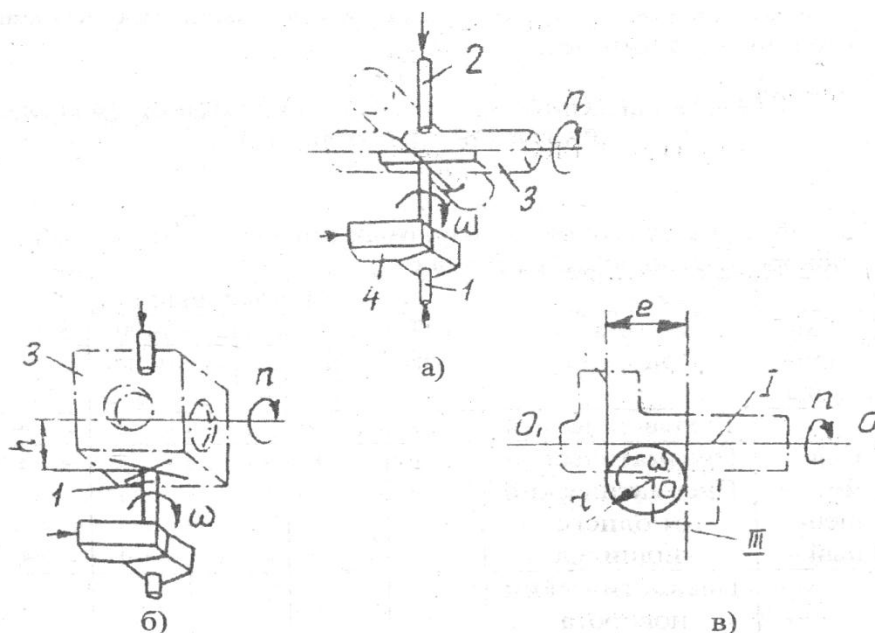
Схемы установки (базирования) и фиксации в угловом положении деталей при многосторонней обработке на токарных станках: а)
